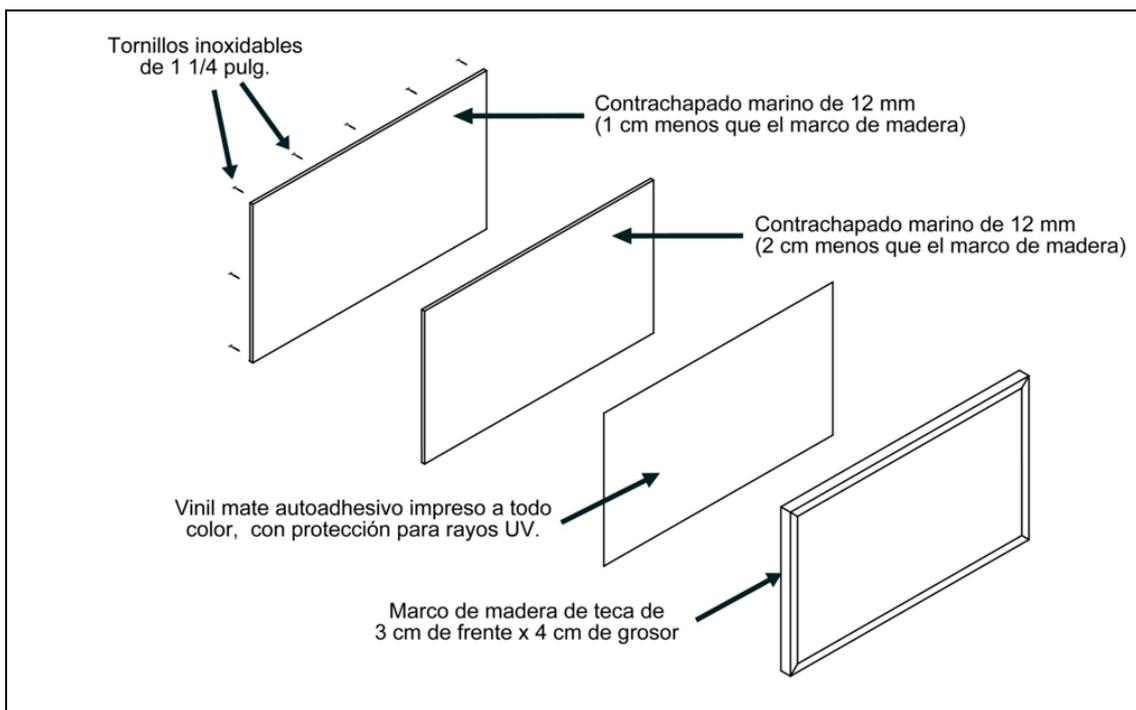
Detalles para la construcción de los paneles interpretativos
